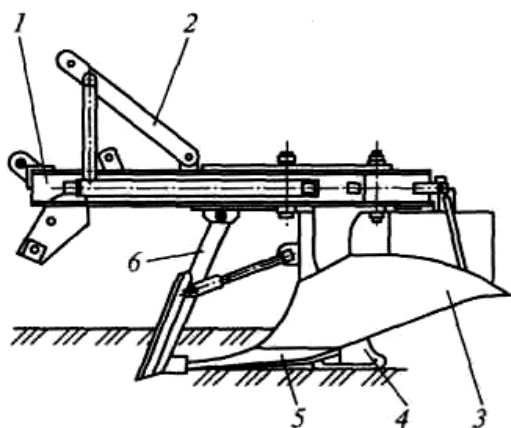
Плуг комбинированный лесной ПКЛ-70:
